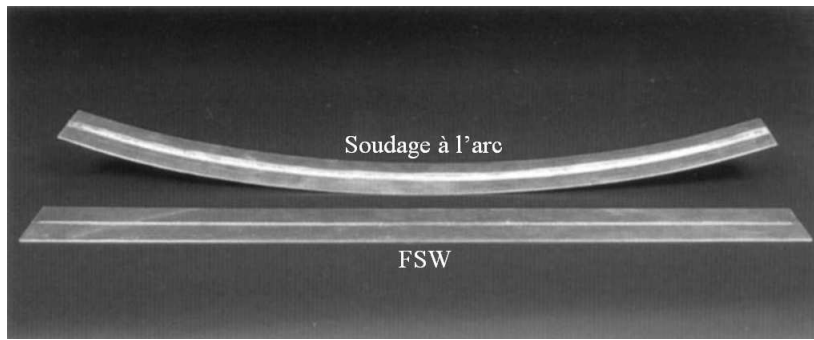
Comparaison de la distorsion entre le soudage FSW et le soudage à l'arc (Référence : Hitachi America, Ltd.)
